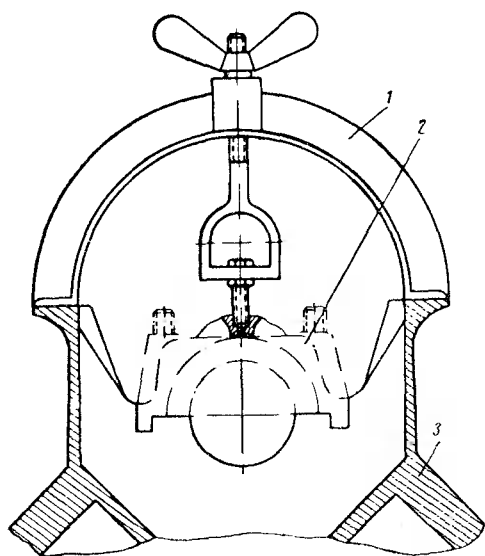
Съемник крышек коренных подшипников и держателя сальника:
